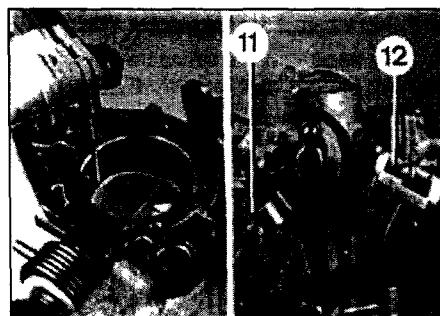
Установка хвостовика сверла для измерения зазоров в приводе пускового устройства
